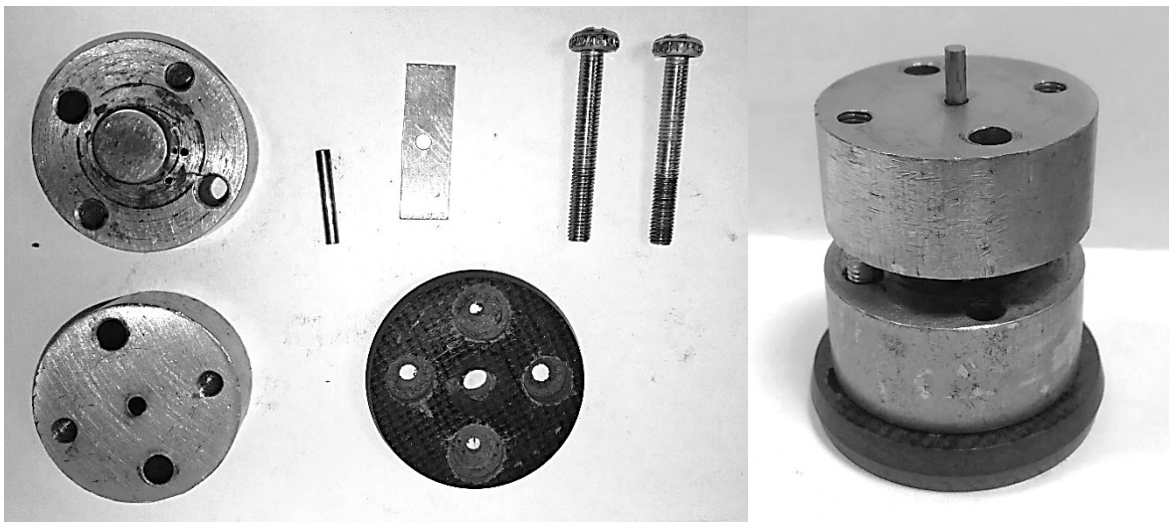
Сборка для прессования в разобранном виде (слева), сборка для прессования в собранном виде (справа)
